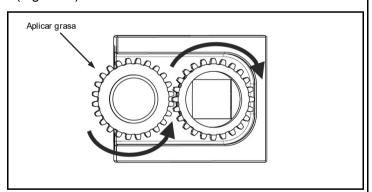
Comprobar que los engranajes giren suavemente, aplicar grasa
